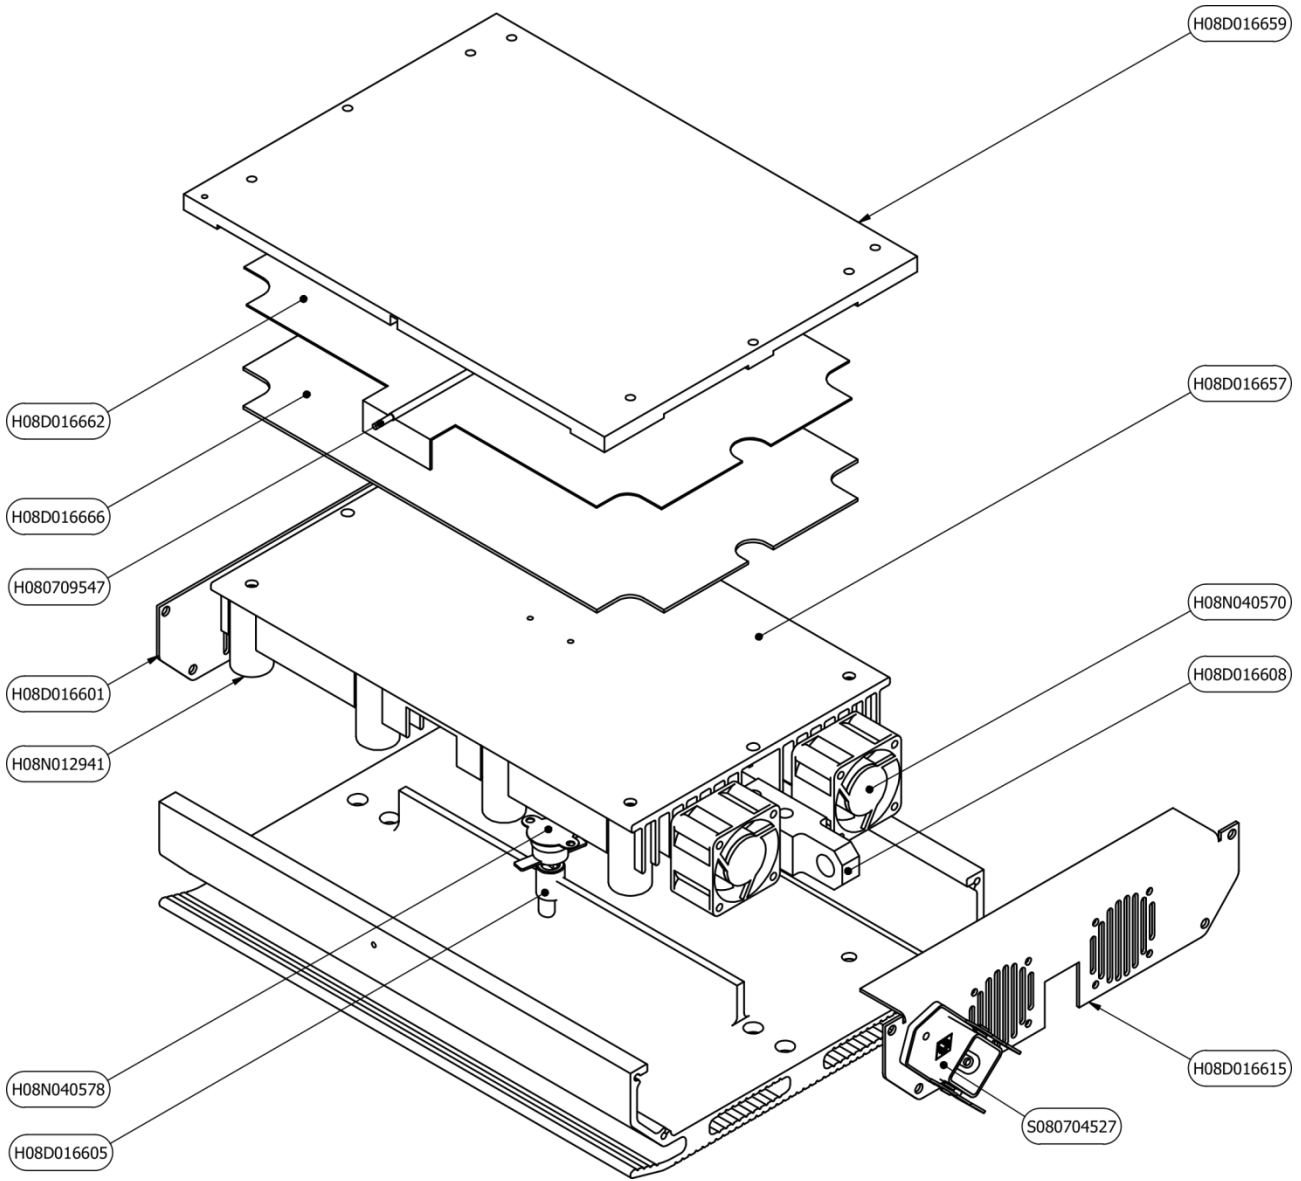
H08D016658 Assemblage de la plaque chauffante inférieure PML-200
